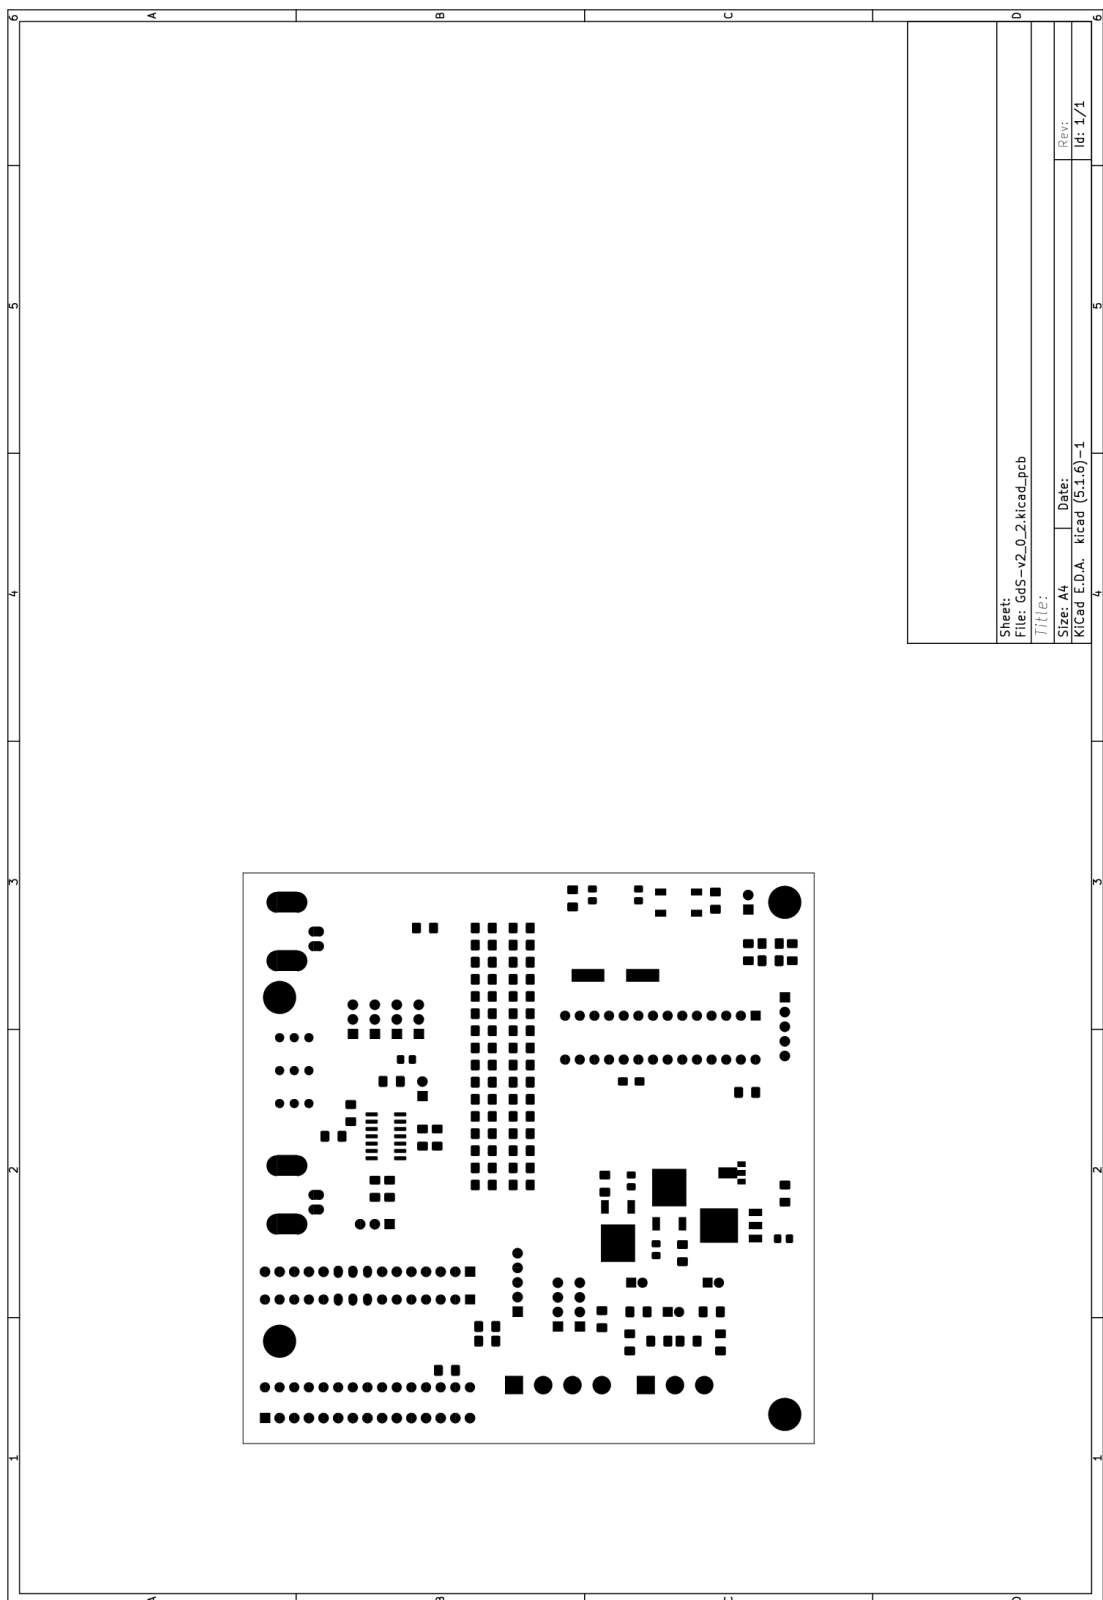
PCB máscara de soldadura (vista superior).
